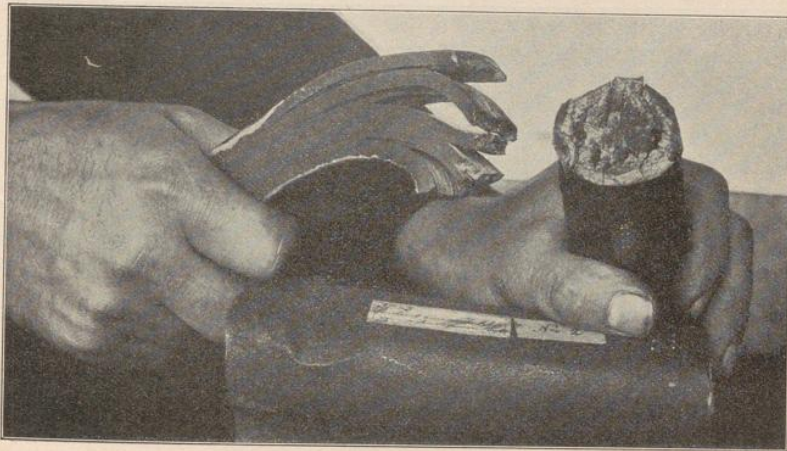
Eisen. Zu Packeten mangelhaft zusammengeschweißte Schweißisenstücke; links aus gelockerten Stäben; rechts mit hohlen Stellen.
